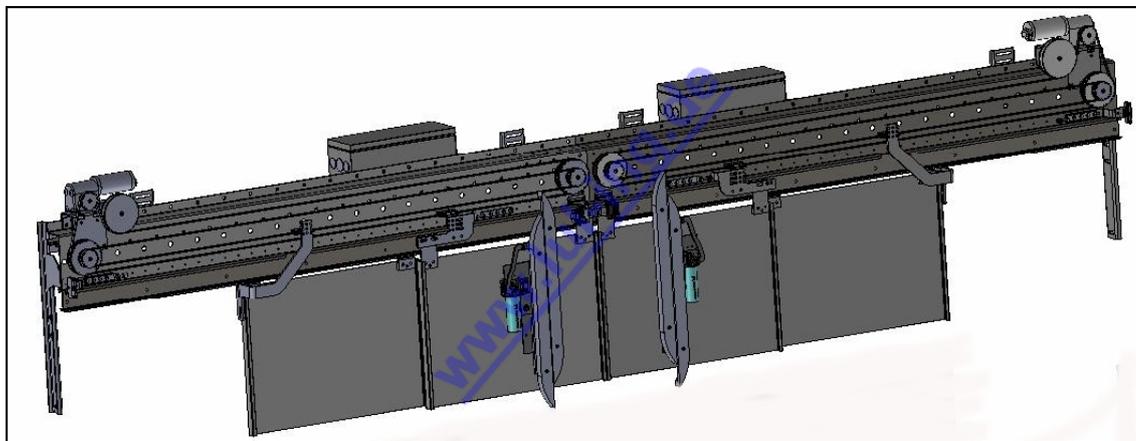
Machine de porte L&L QKS10 – Vue en 3D
